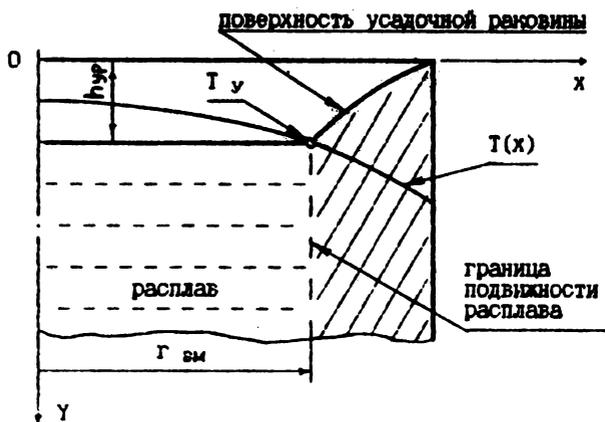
Формирование усадочной раковины при затвердевании расплавленной цилиндрической отливки
